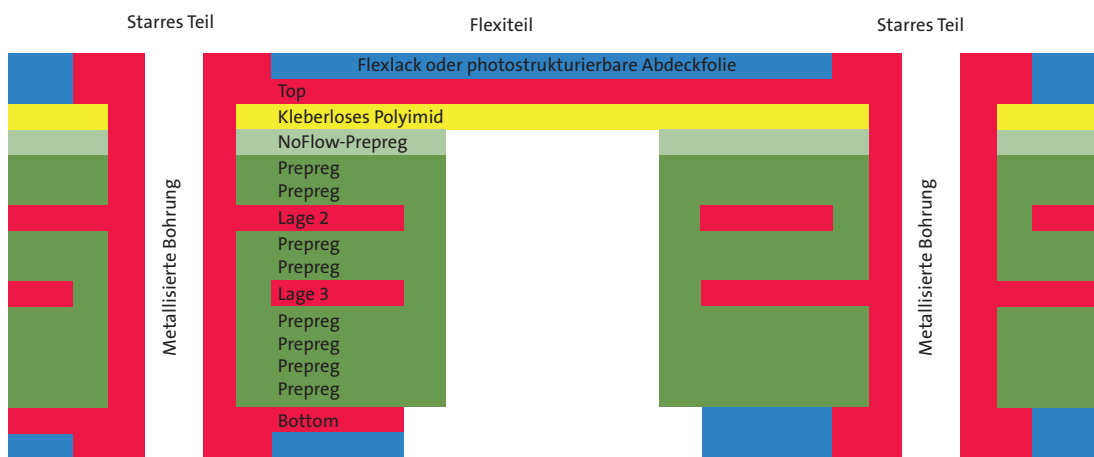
Musteraufbau eines 4-Lagen-Multilayers mit flexibler Top-Lage
